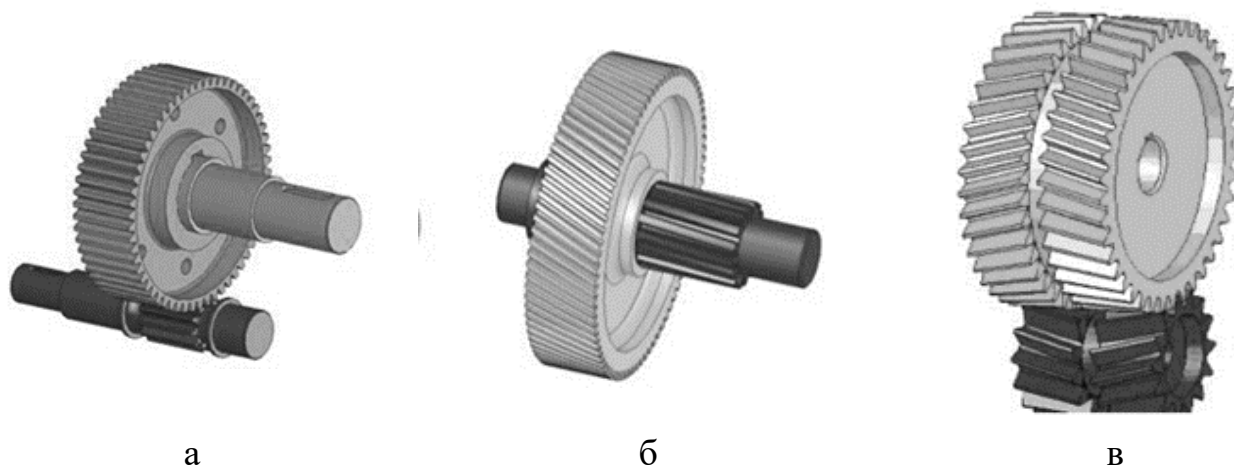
Виды зубчатых передач: а — прямозубая; б — косозубая; в — шевронная.
